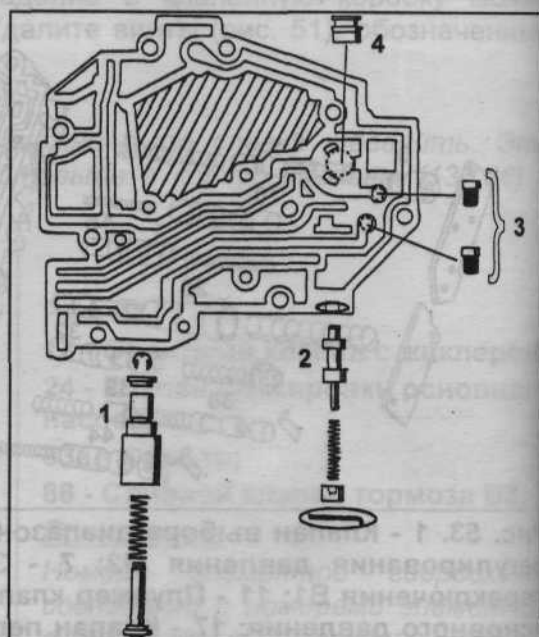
Нижняя часть клапанной коробки. 1 - Клапан блокировки рычага выбора диапазона; 2 - Клапан включения вспомогательного насоса; 3 - Фильтры; 4 - Клапан.
